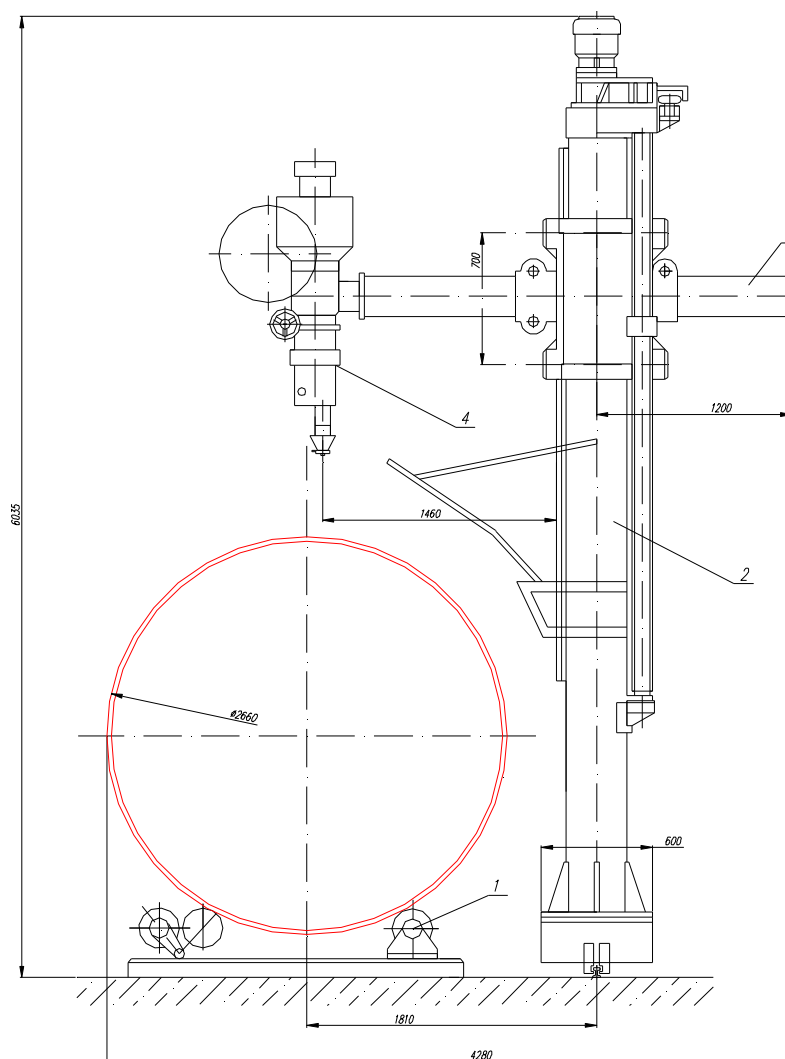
Эскиз установки для сварки кольцевого шва.
